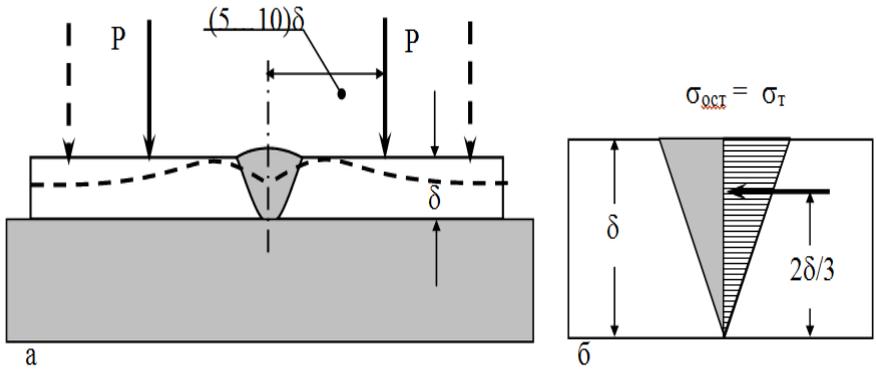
Уменьшение сварочных деформаций за счет жесткого закрепления деталей при сварке.
